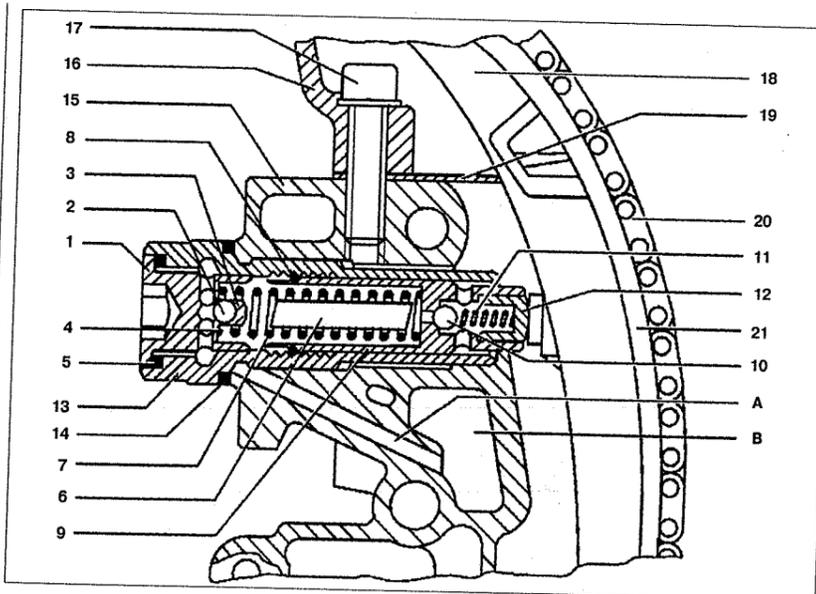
Натяжное устройство цепного привода в разрезе:
